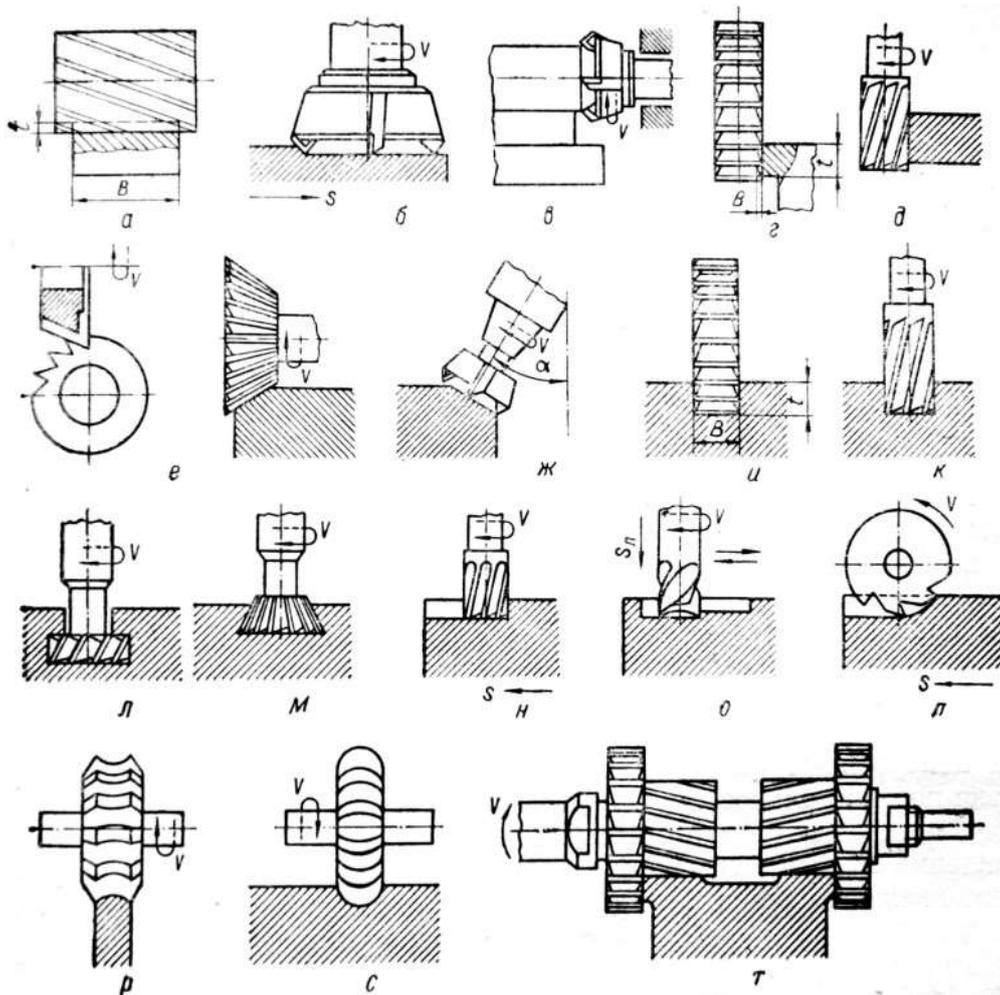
Приклади поверхонь, які обробляють на фрезерних верстатах
